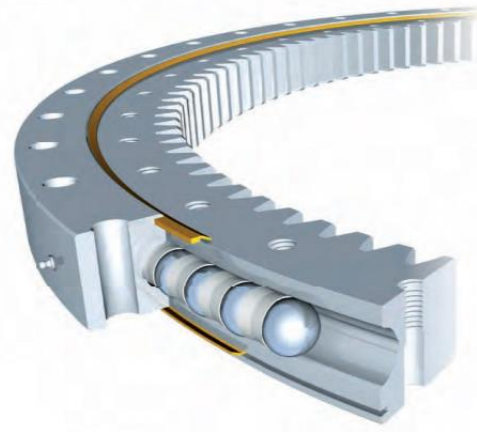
Rodamiento axial de bolas de gran diámetro.
